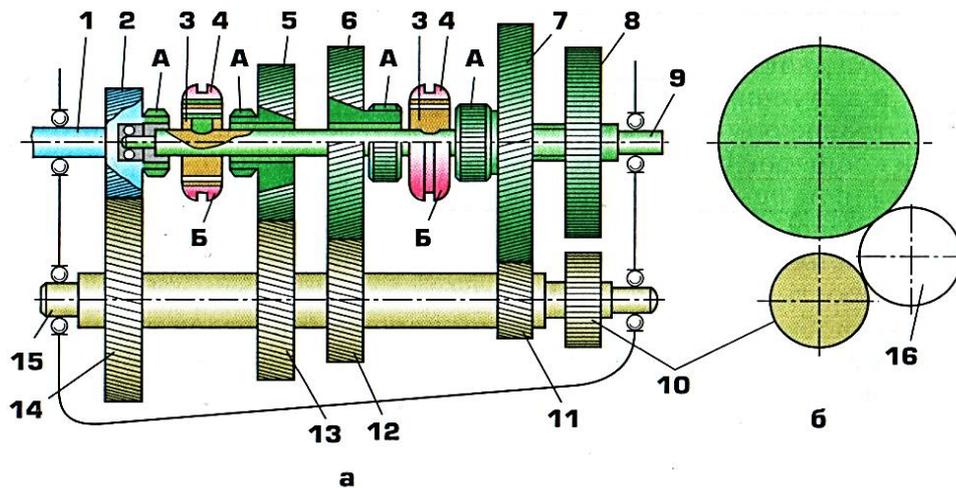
Схема коробки передач с постоянно закрепленными шестернями:
